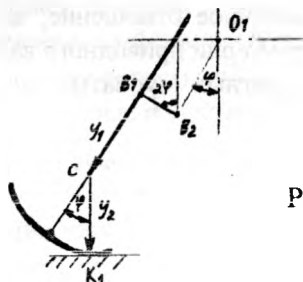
Описание профиля башмака колесно-шагающего движителя
